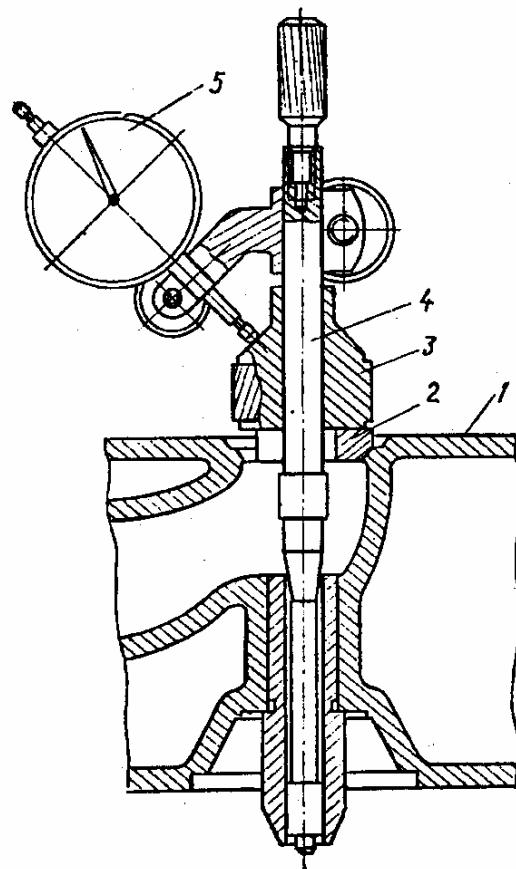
Схема перевірки биття робочої фаски клапанного гнізда відносно поверхні отвору напрямної втулки клапана:
